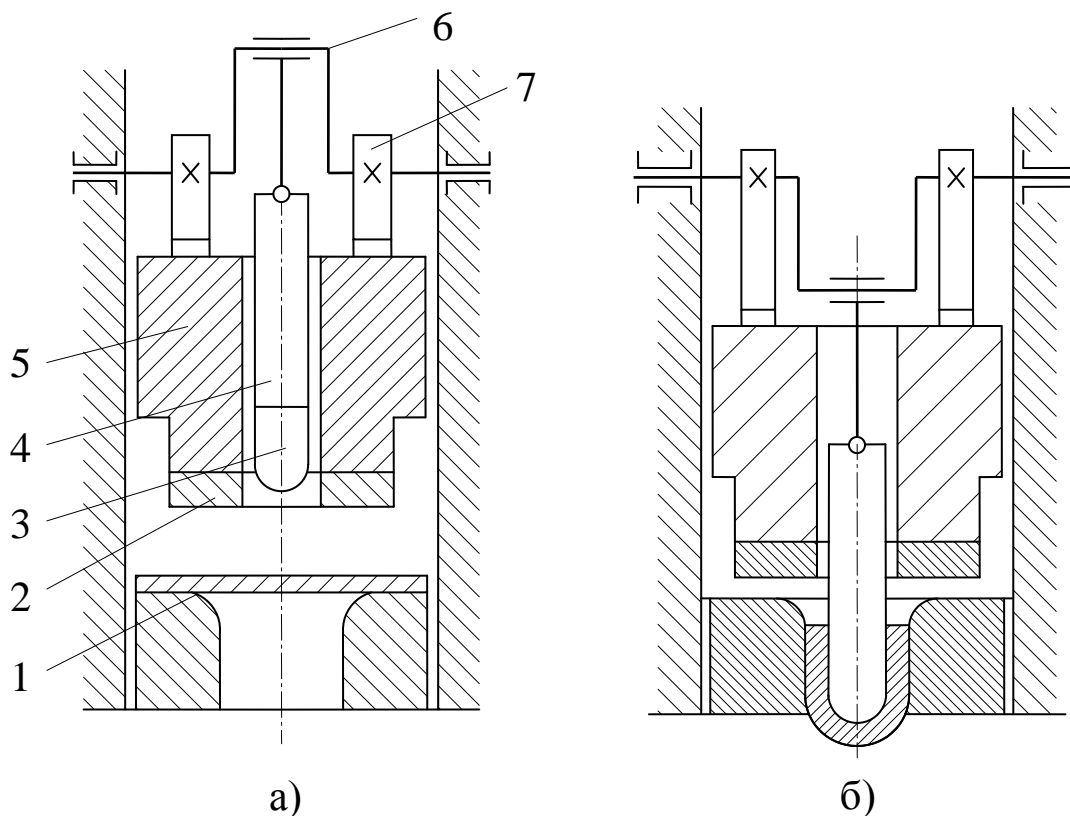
Схема кривошипного преса подвійної дії
